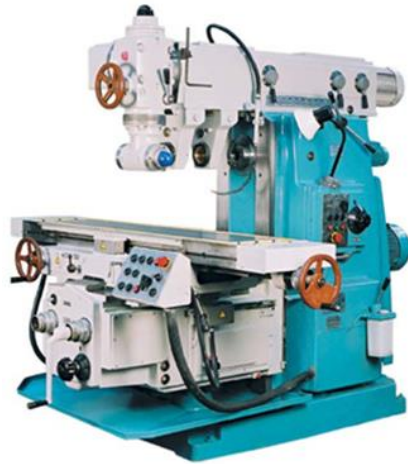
Вертикальний консольно-фрезерний верстат
